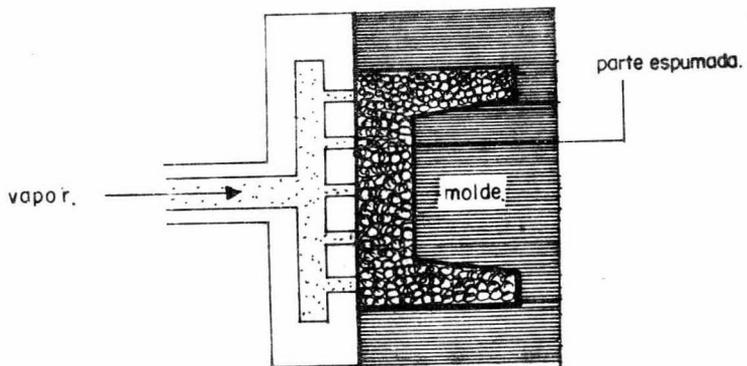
MOLDEO DE POLIESTIRENO EXPANDIBLE.
